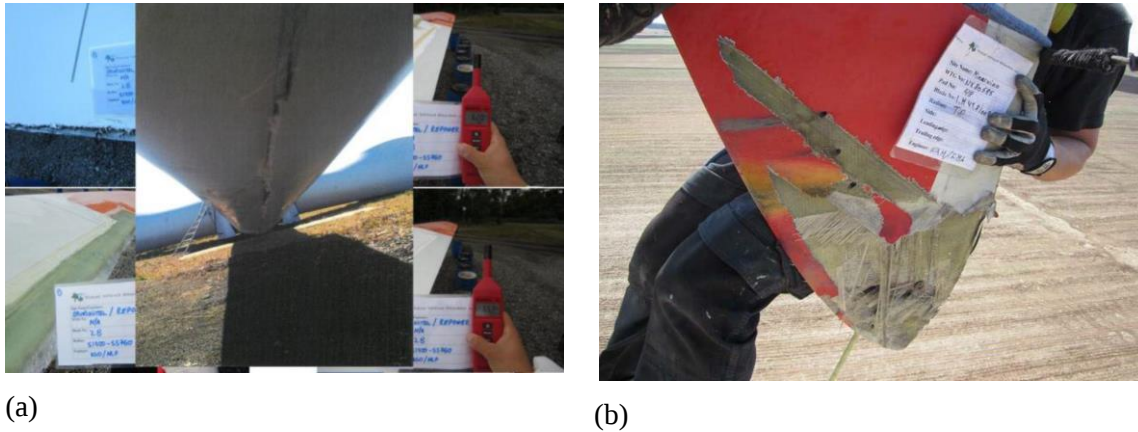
Daños por despegado de los compuestos. (a) Despegado entre las capas y el núcleo, tipo 3; (b) grietas a lo largo de las fibras, tipo 5, y grietas en la resina, tipo 7 [2].
